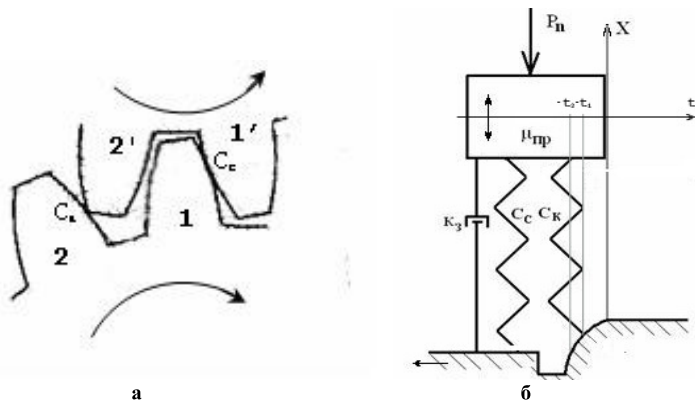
Эквивалентная динамическая схема зубчатой пары:
